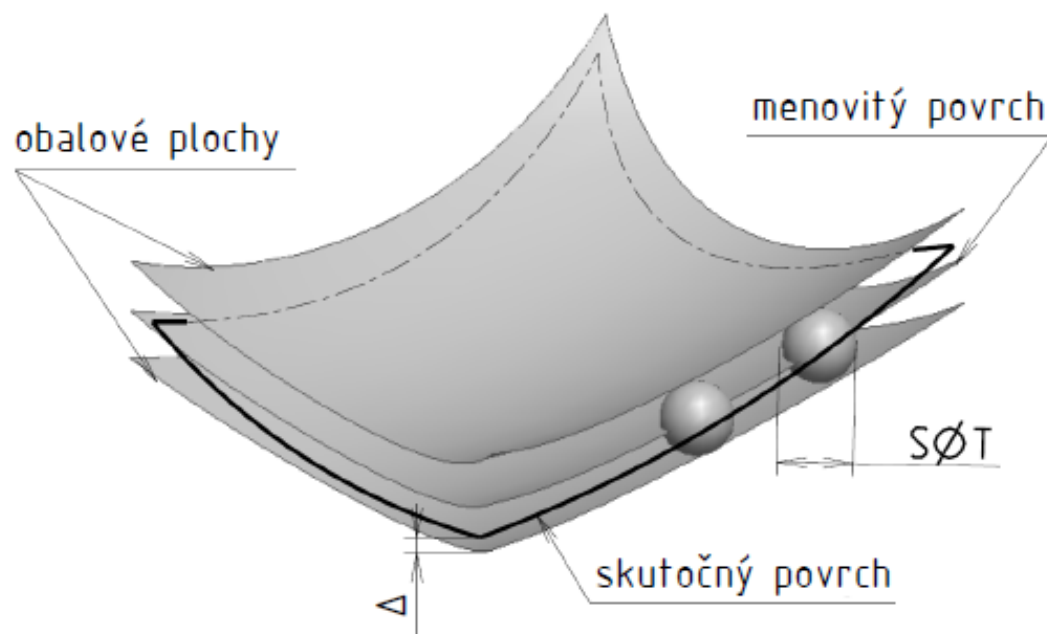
Tolerancia tvaru profilu predpísaná vzhľadom na základný systém
